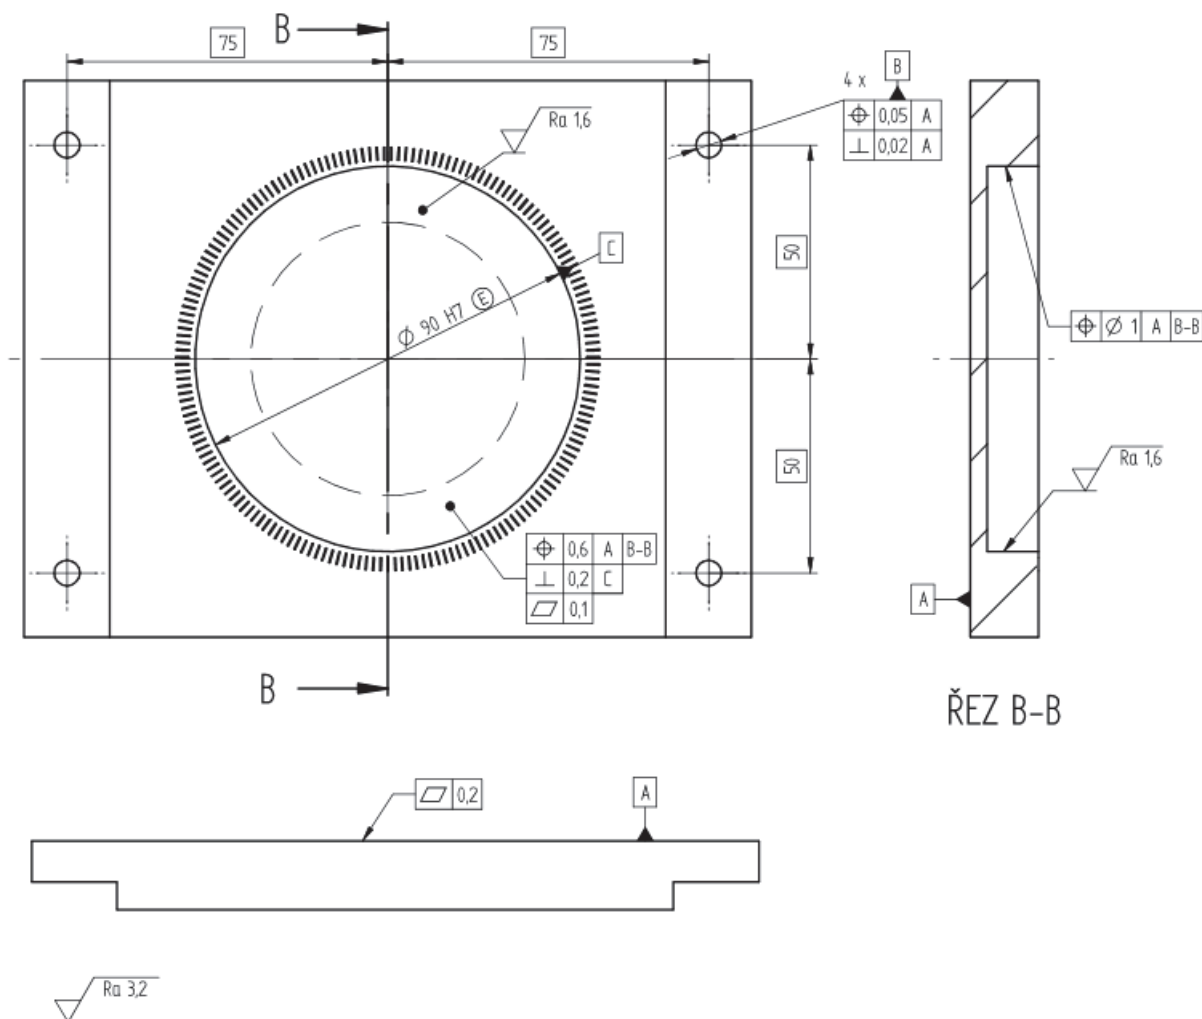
Tolerance hran pro součást "podstava"
